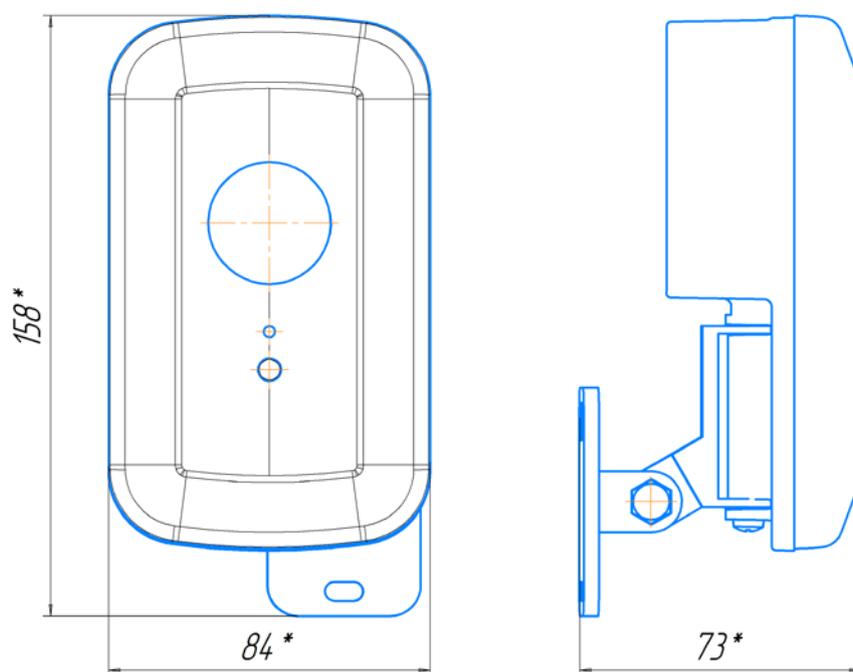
Оповещатель пожарный взрывозащищенный звуковой, комбинированный
